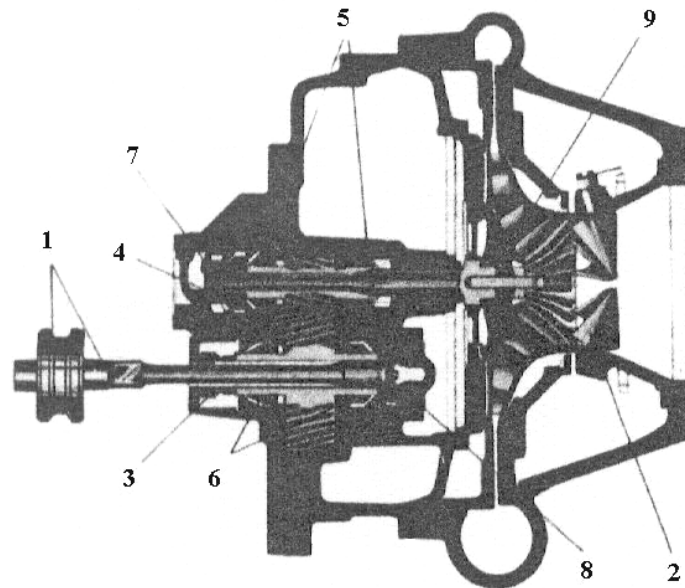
Compresor centrifugal deschis cu multiplicator încorporat
